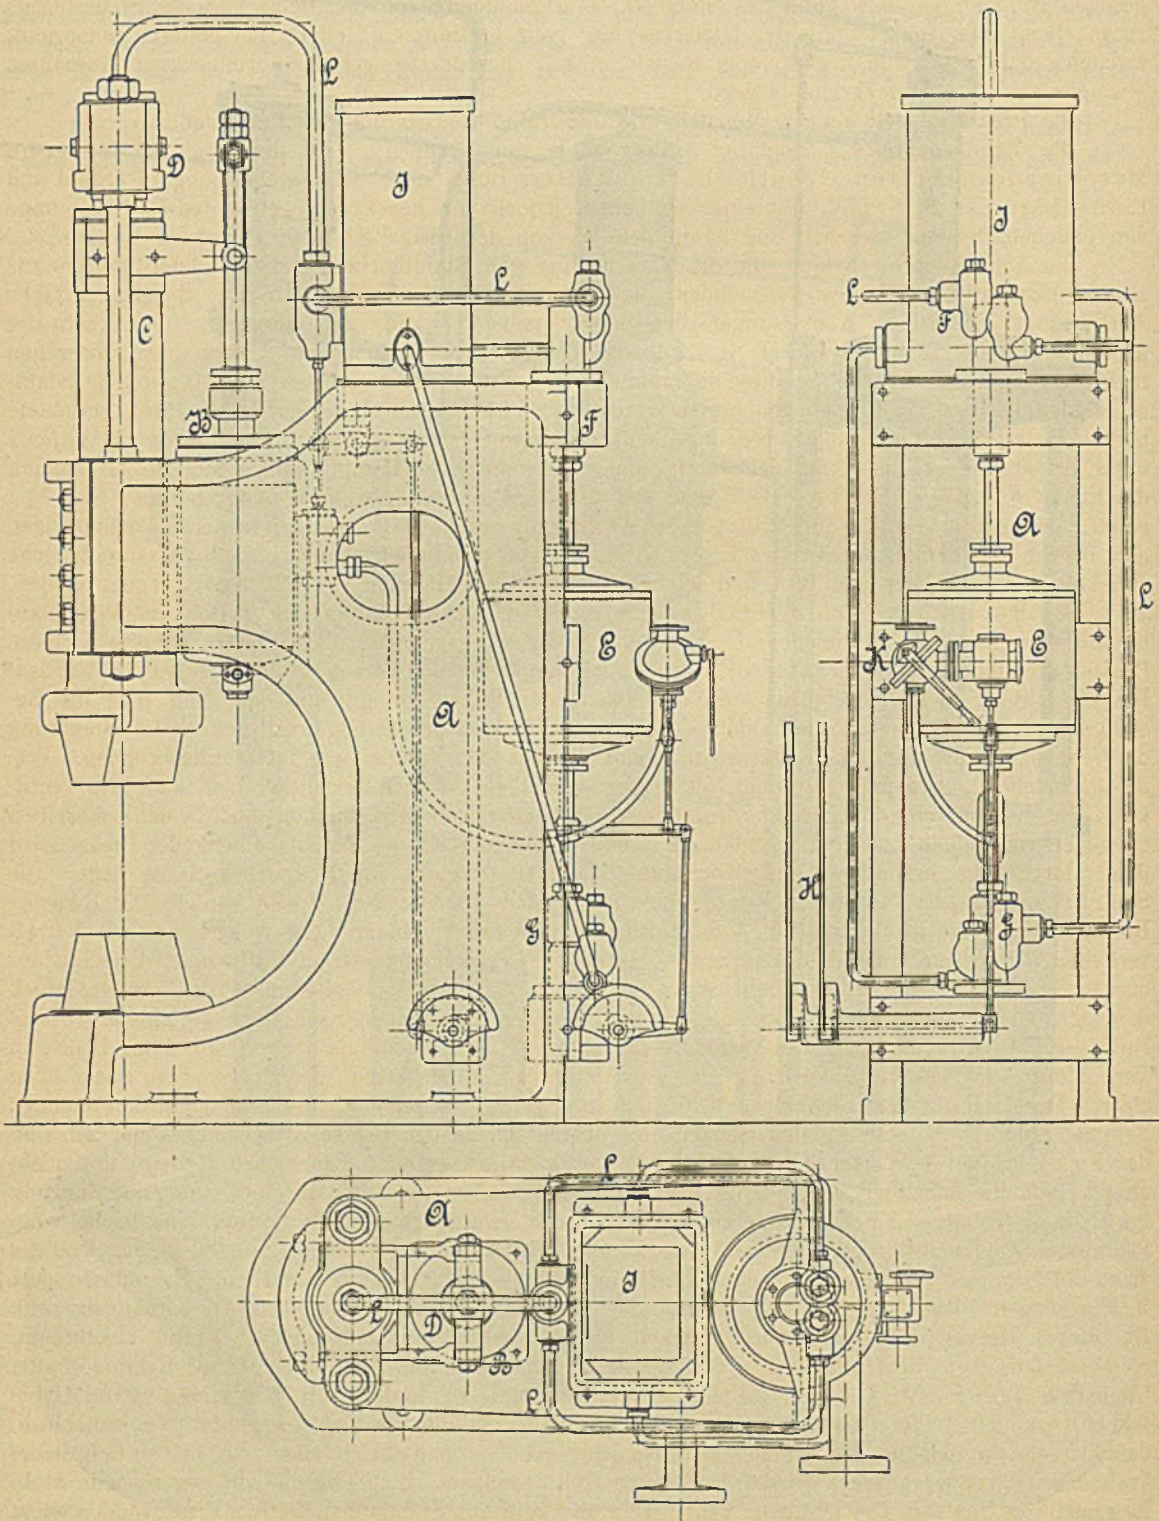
c. Schmiedepresse der Duisburger Maschinenbau-A.-G.
